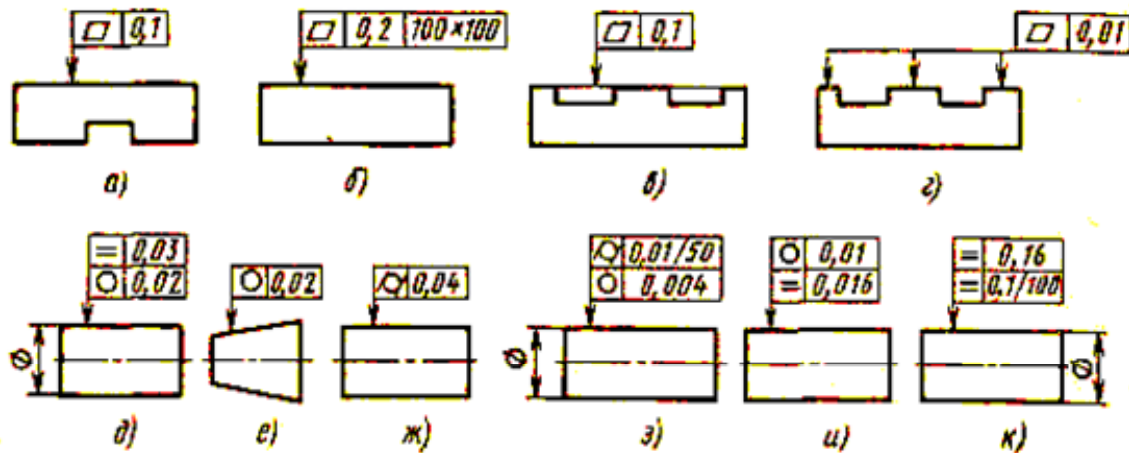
Условные обозначения допуска формы поверхностей детали
